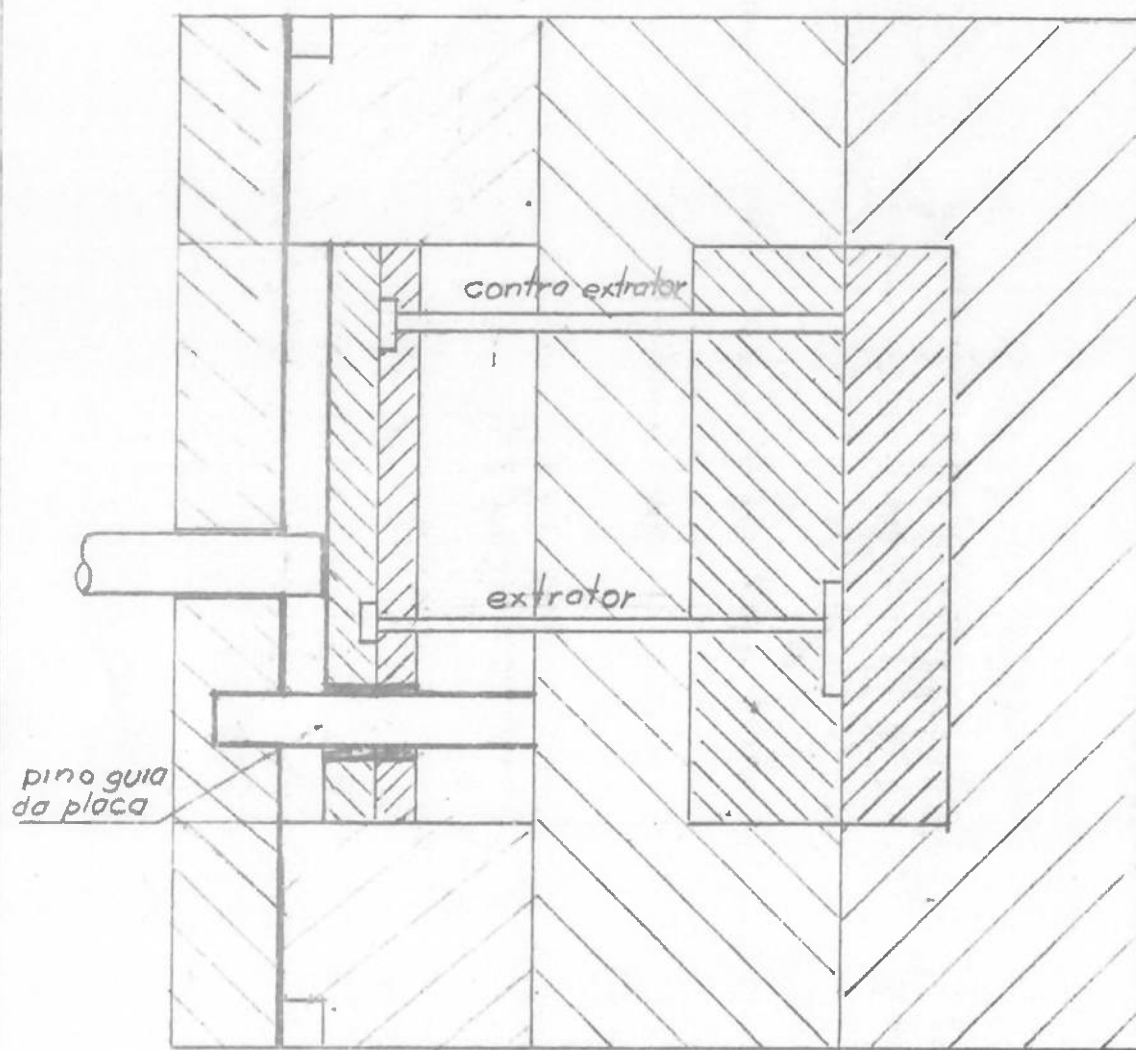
Corte de um molde esquemático mostrando um extrator, um contra extrator, a placa extratora guia, a placa extratora de encosto, pino de guia das placas extratoras.
